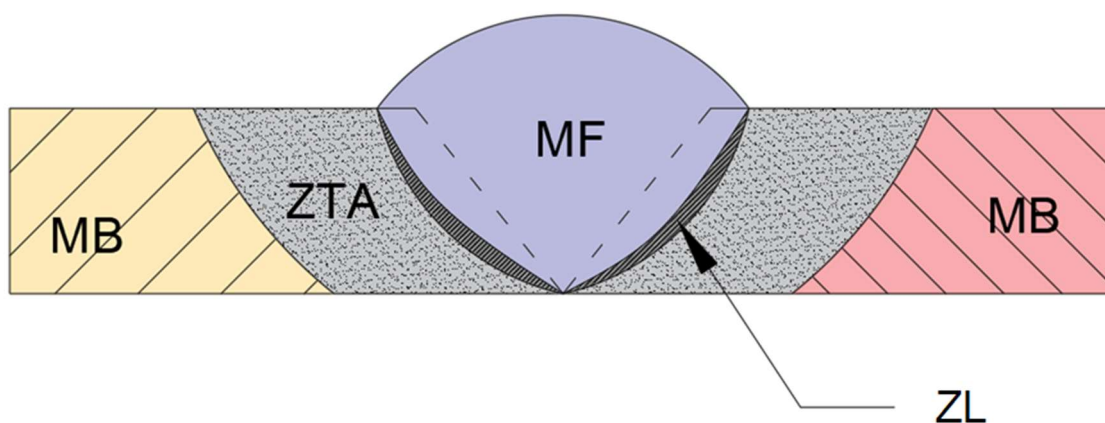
Ilustração esquemática das zonas afetadas pelo calor durante um processo de soldadura.
